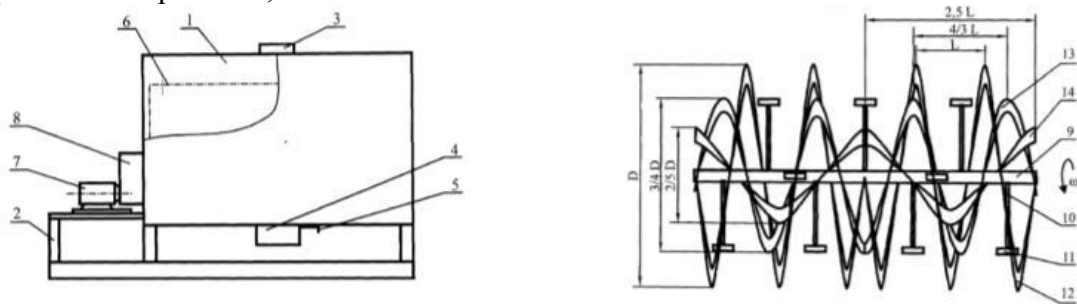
Змішувач за патентом № 2488434: а – конструкційна схема; б – комбінований шнек; 1 – бункер; 2 – рама; 3, 4 – завантажувальний і розвантажувальний патрубків; 5 – заслінка; 6 – комбінований шнек; 7 – двигун; 8 – редуктор; 9 – вал; 10 – стрижні; 11 – елементи стрічкової спіралі; 12 – зовнішній стрічковий шнек; 13 – середній стрічковий шнек; 14 – внутрішній стрічковий шнек.
